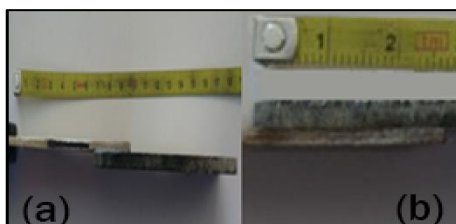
(a) Soldagem do alumínio 2024 e compósito PEI/fibra de vidro por GLP; (b) detalhe da junta soldada.
